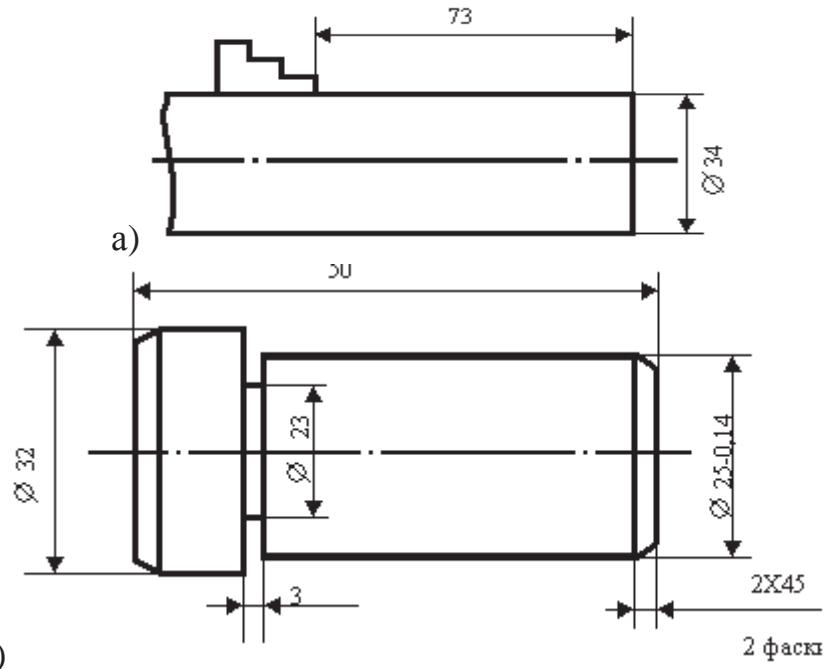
Заготовка для деталі «палець» (а) і готова деталь (б)
